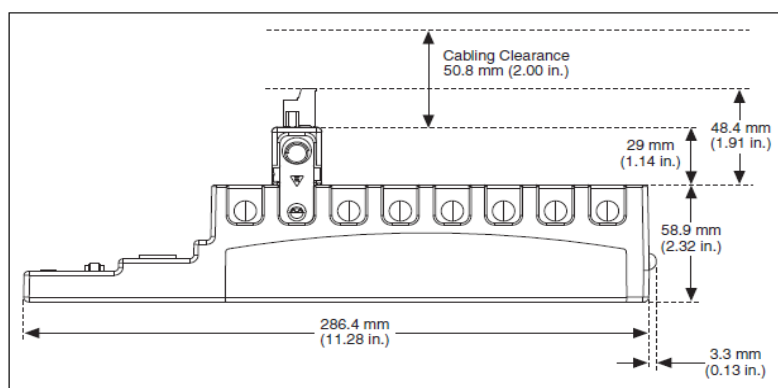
cRIO-9074, Vista Inferior con Dimensiones
